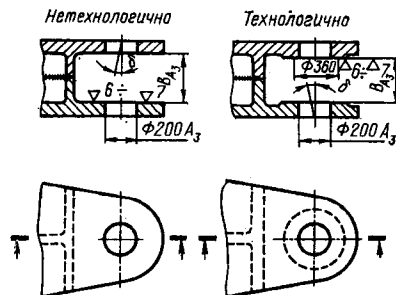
Выполнение мест сопряжений, обрабатываемых в узлах после сварки.
